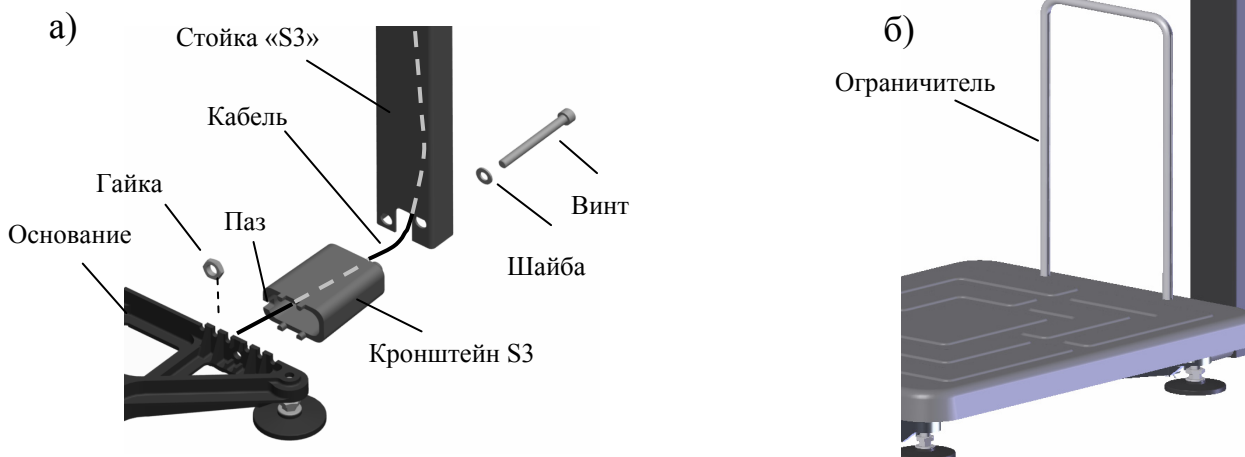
Крепление прямоугольной стойки к модулю ТВ-S
